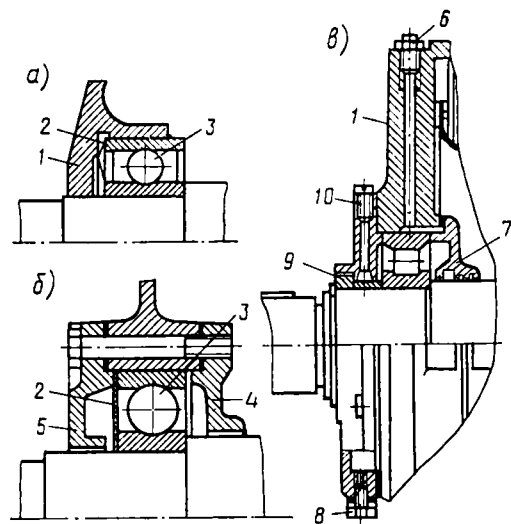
Подшипниковые узлы с шарикоподшипниками с двусторонним уплотнением (а), с двумя крышками (б), с устройством для пополнения смазки (в):
